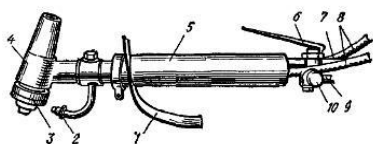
Резак РДМ-2-66 для плазменно-дуговой резки
